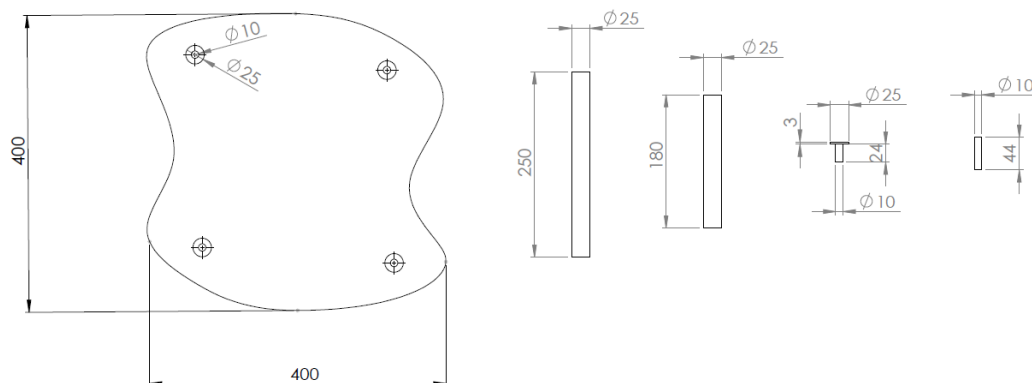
Propuesta 3, dimensiones. Elaboración propia
